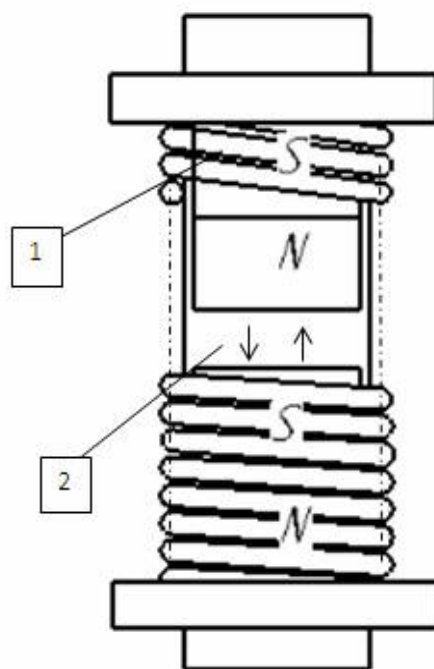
Конструктивно-технологічна схема додаткової генераторної установки: 1- обмотка статора, 2 – повітряний відштовхувальний зазор між двома постійними магнітами.
